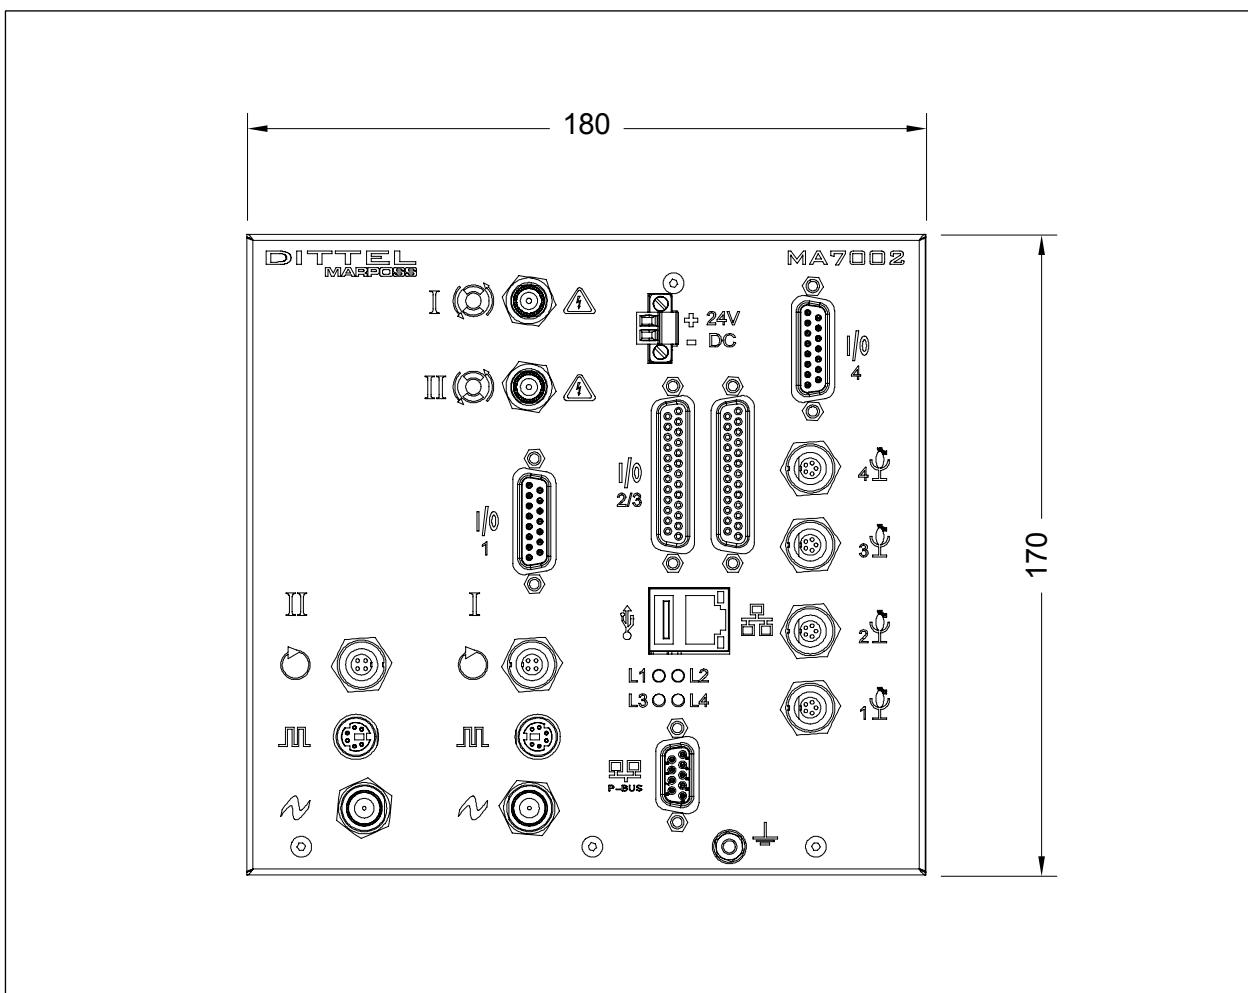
MA7002 Frontansicht – Abmessungen in mm (Abmessungen identisch für M7002)
